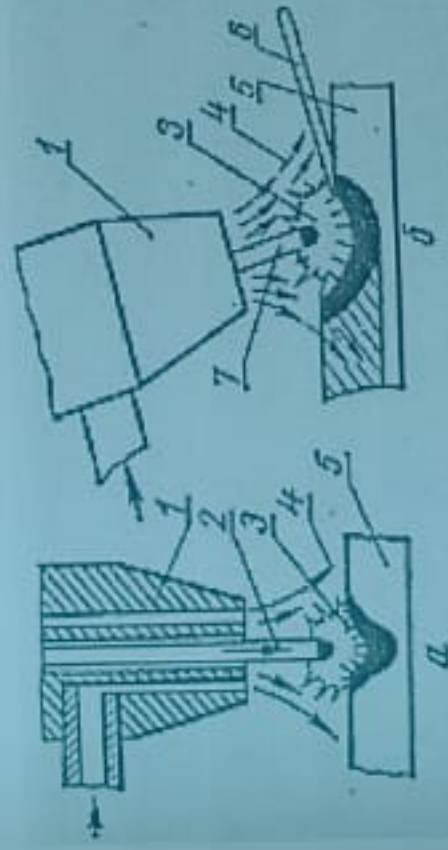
Схемы способов сварки (наплавки) в среде защитных газов:
